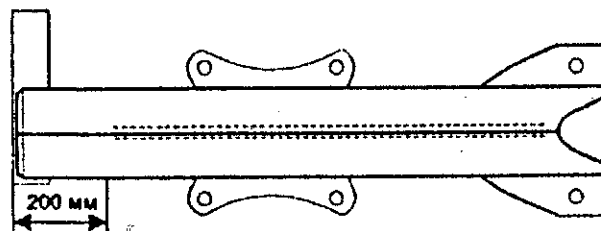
Контроль сварного шва верхней стенки продольной балки рамы
